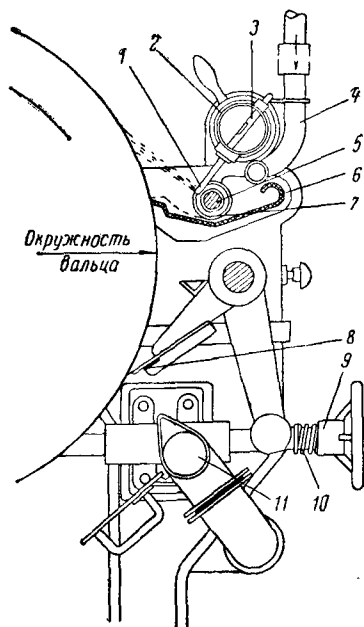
Схема устройства для подачи молока на вальцы распылением: 1—сопло; 2 и 11—воздуховоды; 3—поперечная трубка; 4—молокопровод; 5—вал; 6—желоб; 7—диск; 8—нож; 9—штурвал прижима ножей; 10—пружина.
